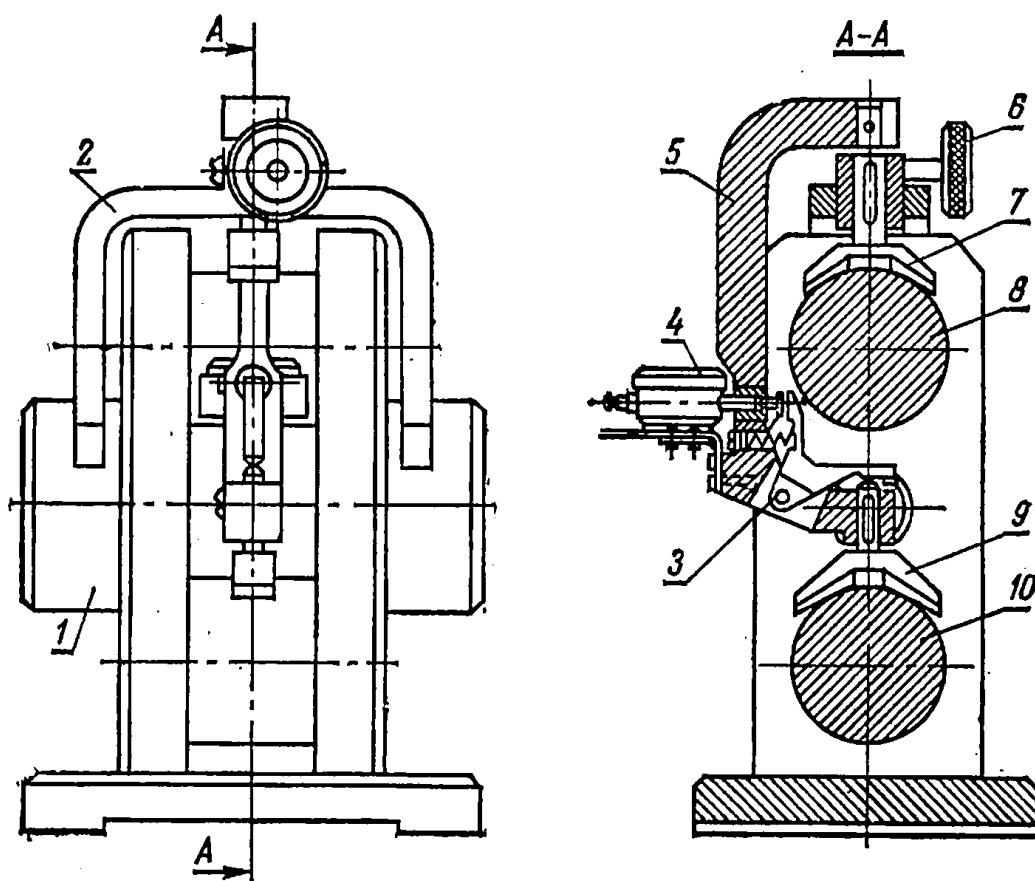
Схема индикаторного приспособления для контроля ра-
